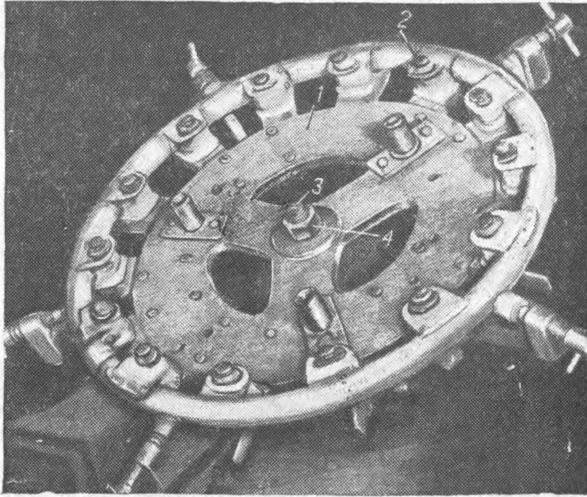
Приспособление для сборки и прихватки патрубков к цилиндру.
